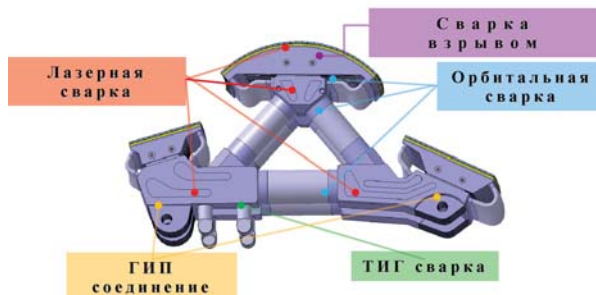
Схема сварки центральной сборки дивертора ИТЭР [3].
